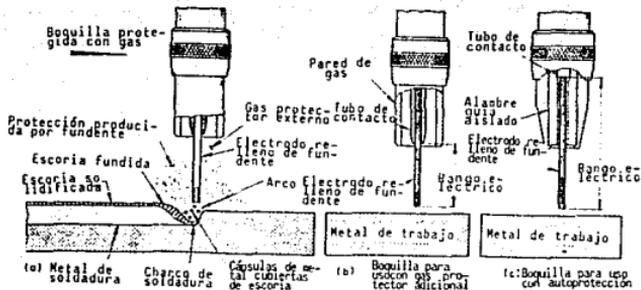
(a) Principios de operación para soldadura por arco con electrodo relleno de fundente con gas de protección auxiliar; (b) y (c) boquillas para gas de protección adicional y para autoprotección.
